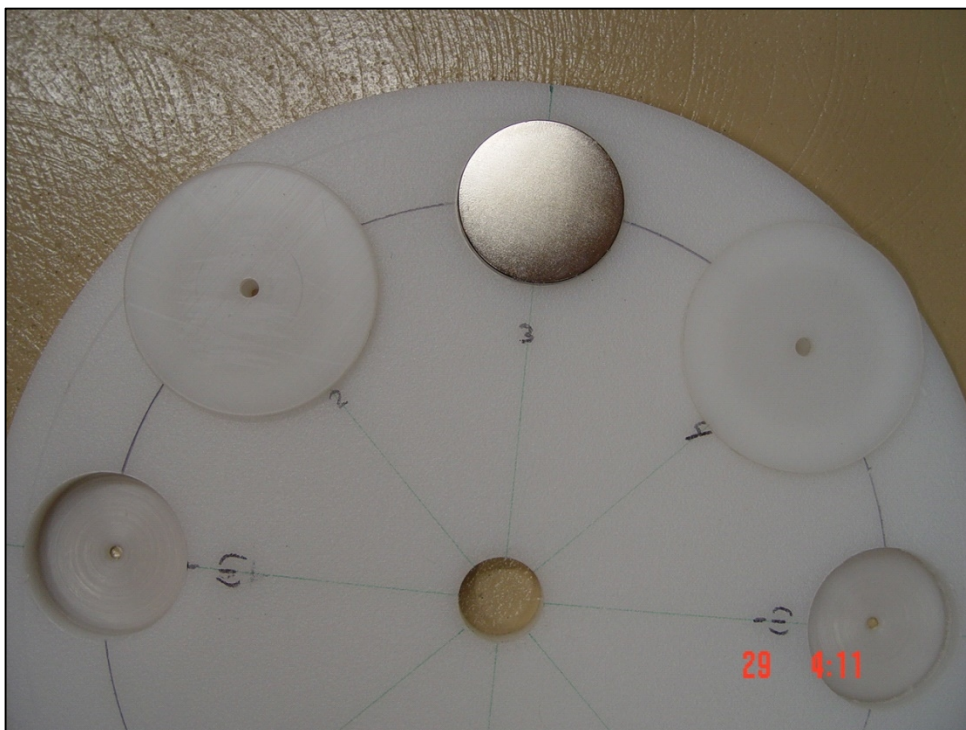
Photo d'un disque du rotor en état d'assemblage
